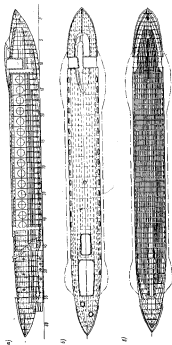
Конструктивные схемы корпуса и надстройки теплохода «Майка»: а — продольный разрез; б — план днища; в — план деки.
